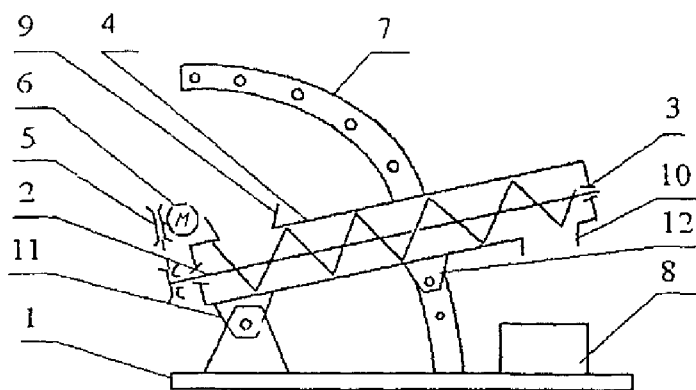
Учебный прибор для демонстрации работы винтового конвейера: 1 – рама; 2 – винтовые витки; 3 – подшипники; 4 – цилиндрический кожух; 5 – ременной вариатор; 6 – электродвигатель; 7 – дуга; 8 – емкость; 9 – загрузочное окно; 10 – разгрузочное окно; 11, 12 – кронштейны
